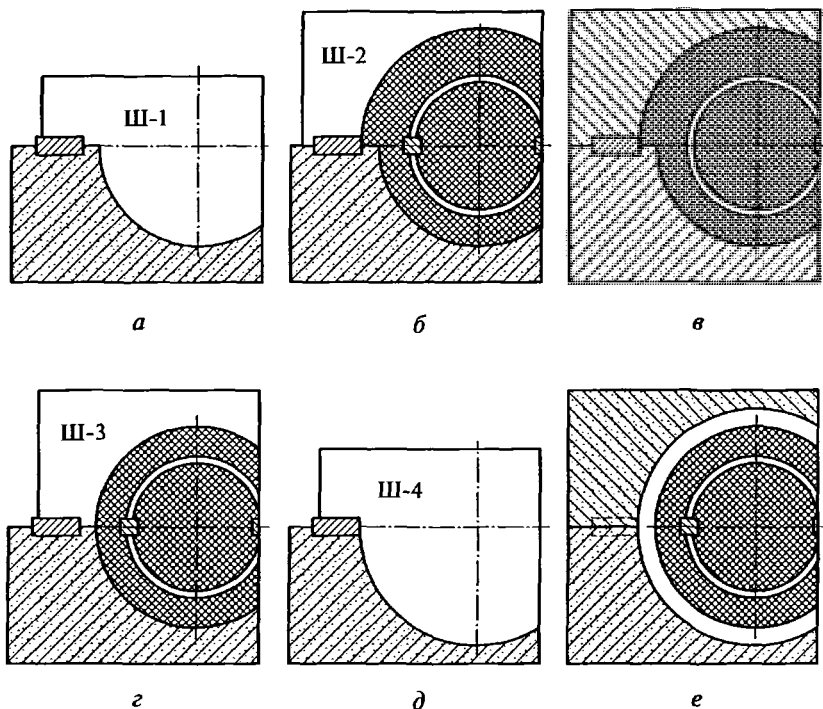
Формовка патрубка с фланцем протяжными шаблонами:
